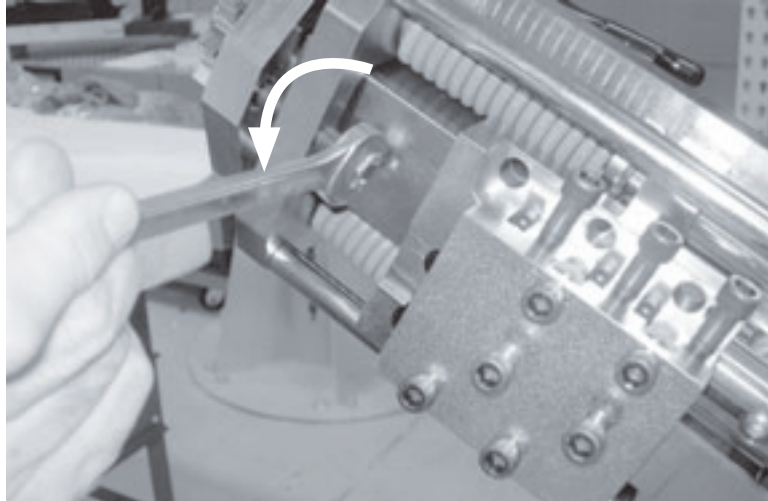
Retrarre le viti di tensione della molla a fondo per caricare a molla le slitte.
